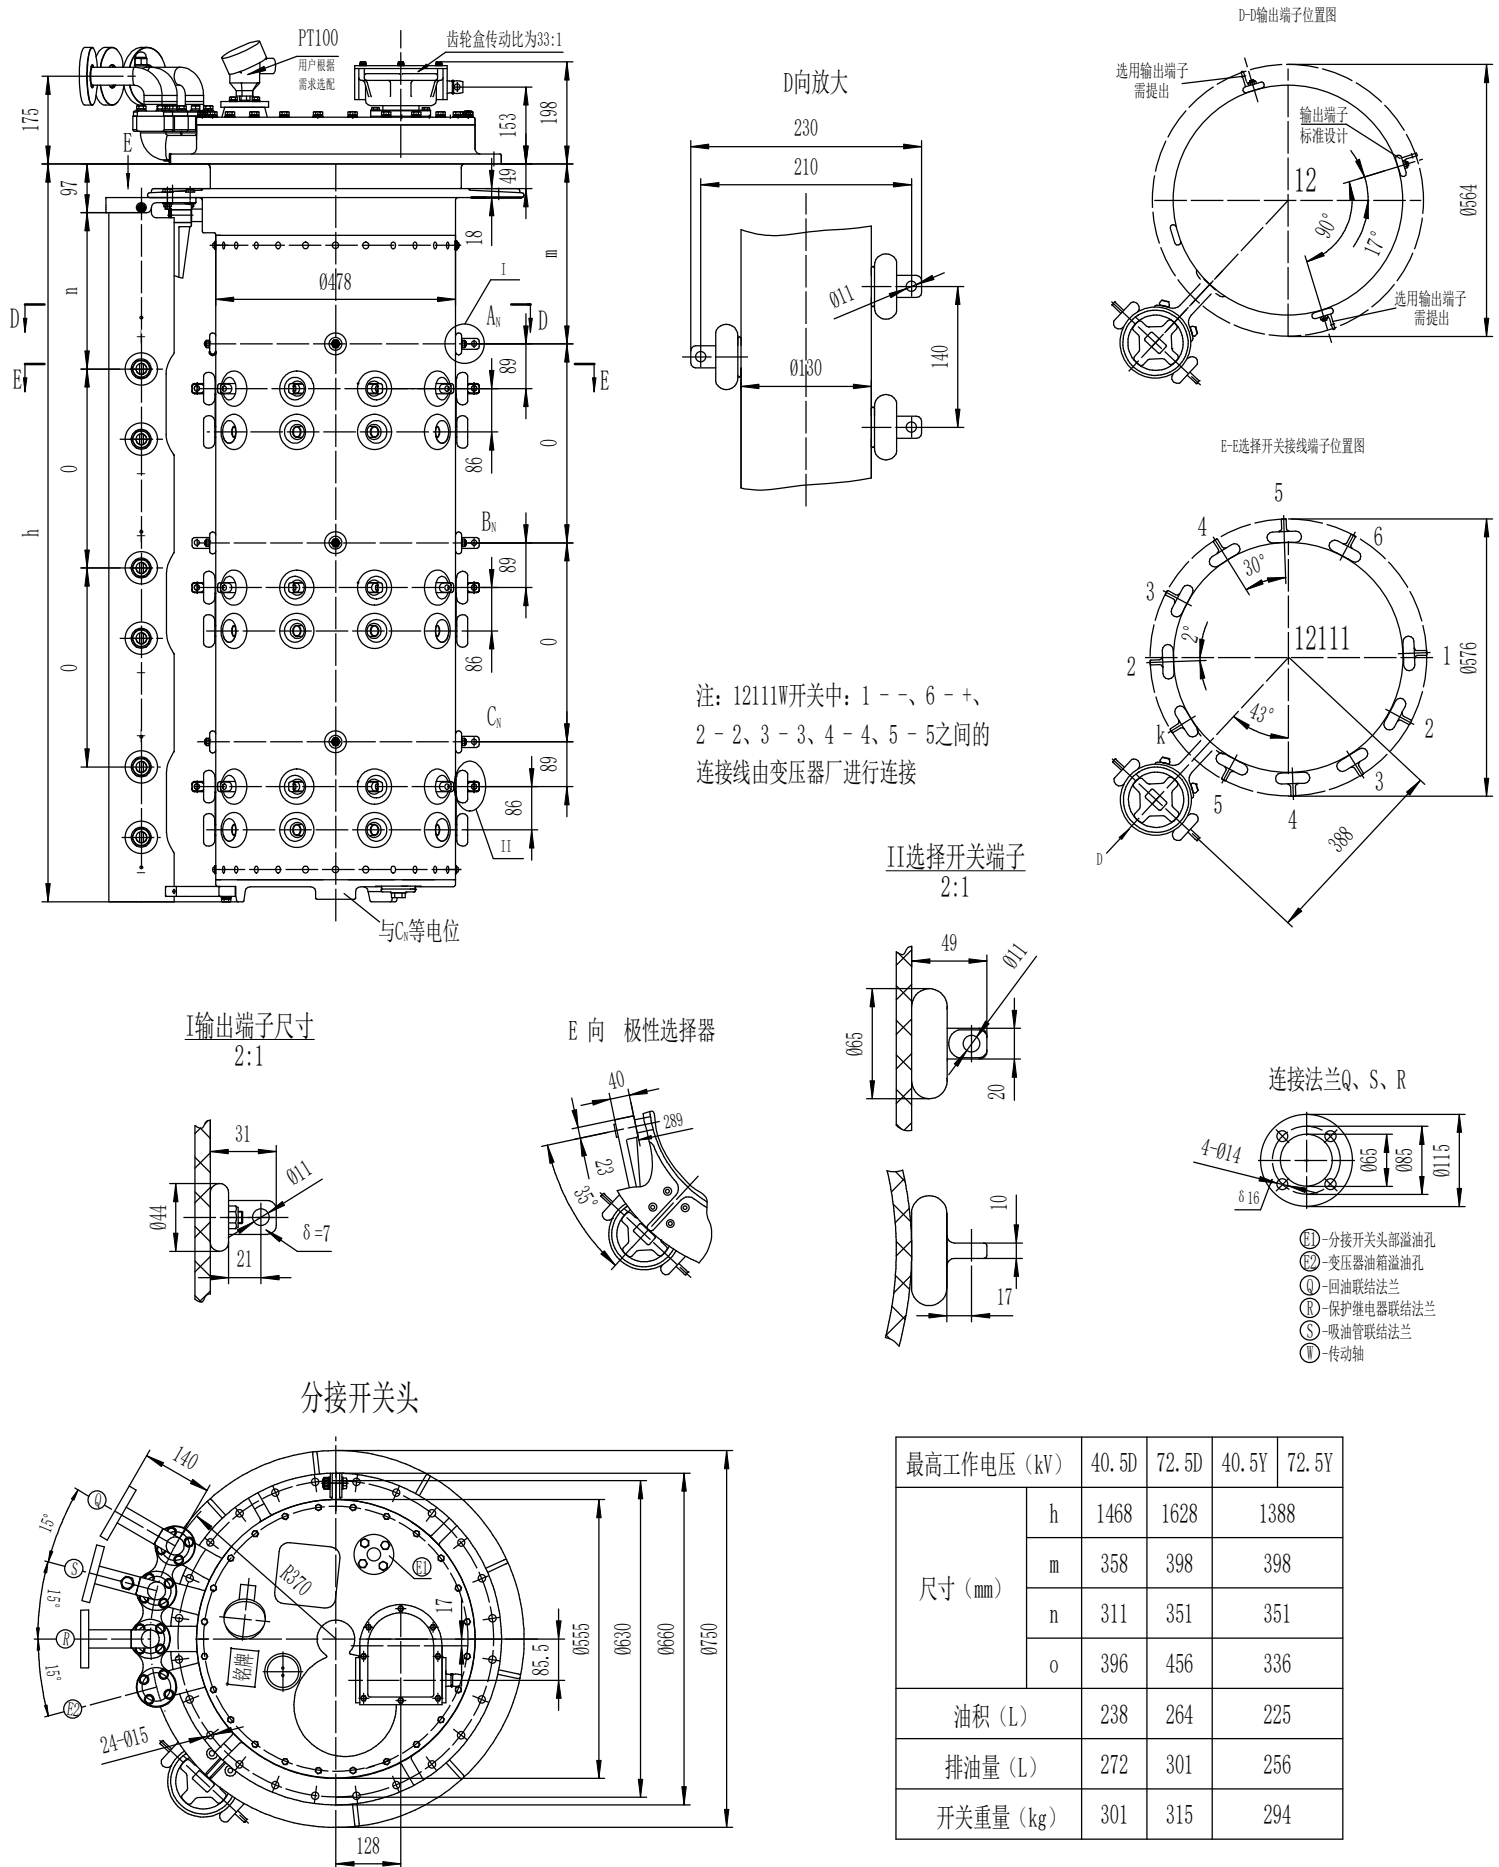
ZVDIII350/500/600 121111带转换选择器外形尺寸图
